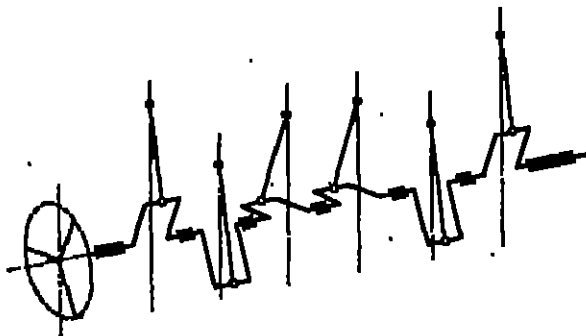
Kurbelwellen der Sechszylindermaschine.
